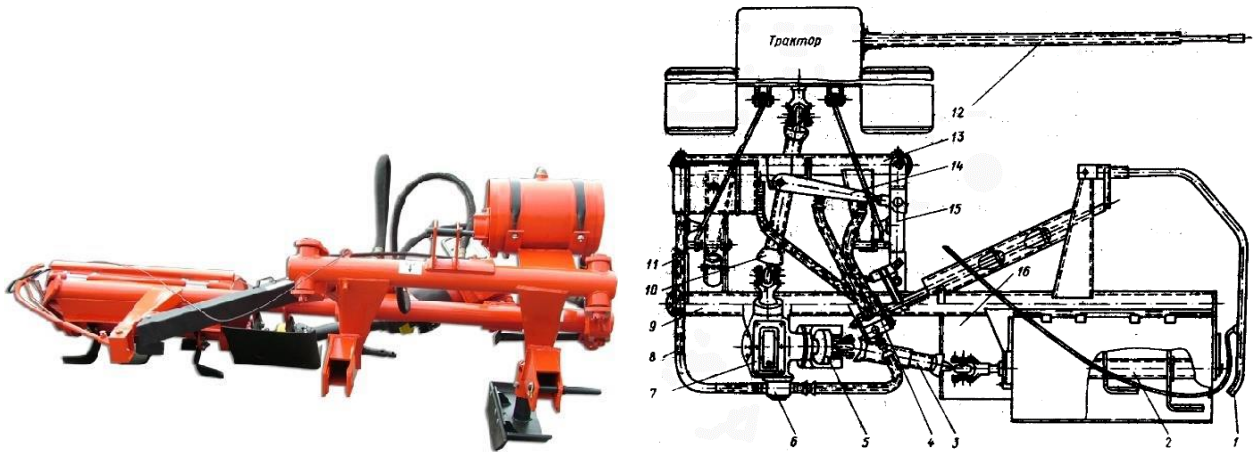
Загальний вигляд і схема фрези садової ФА-0,76:
